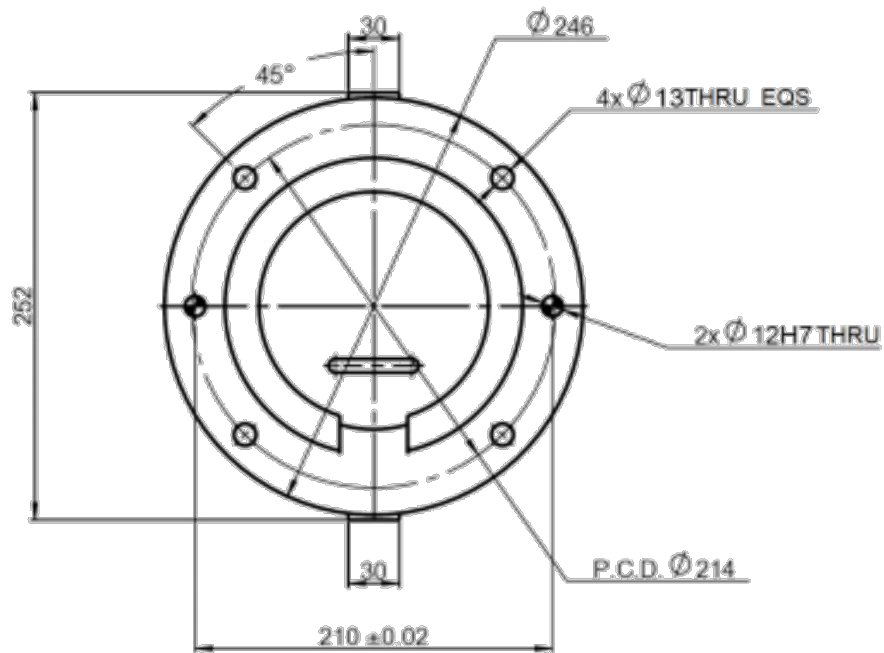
Размеры базы робота ЯКА Pro 16
